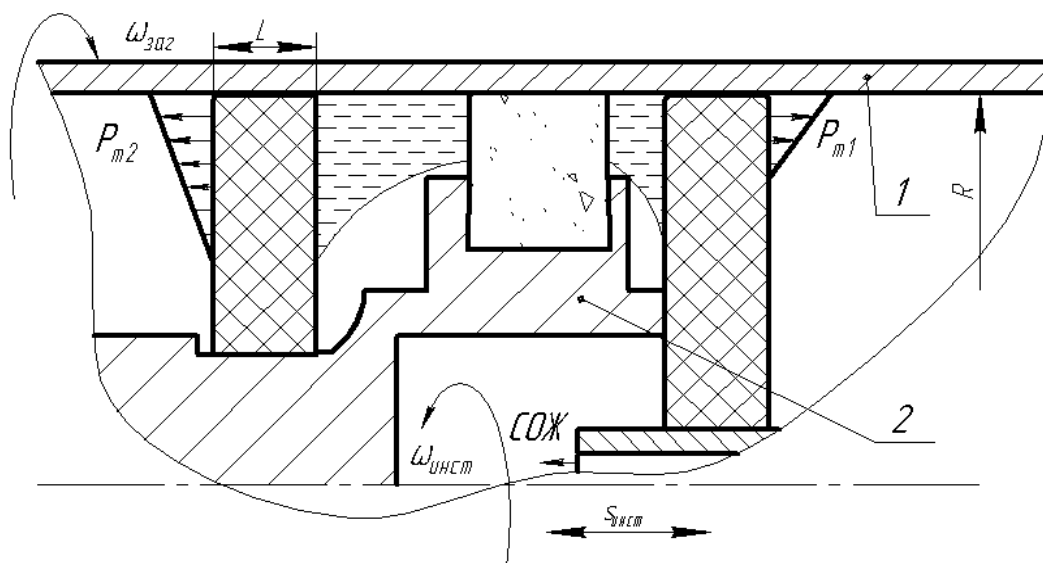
Давление СОЖ на боковые торцы (1 – Заготовка; 2 – Соосный инструмент с торцовыми уплотнениями).
